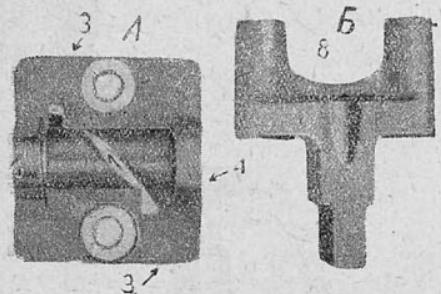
А—кондуктор-рамка для нарезки масляных канавок в подшипниках. Б—державка, употребляемая при нарезке канавок в крышках подшипников
